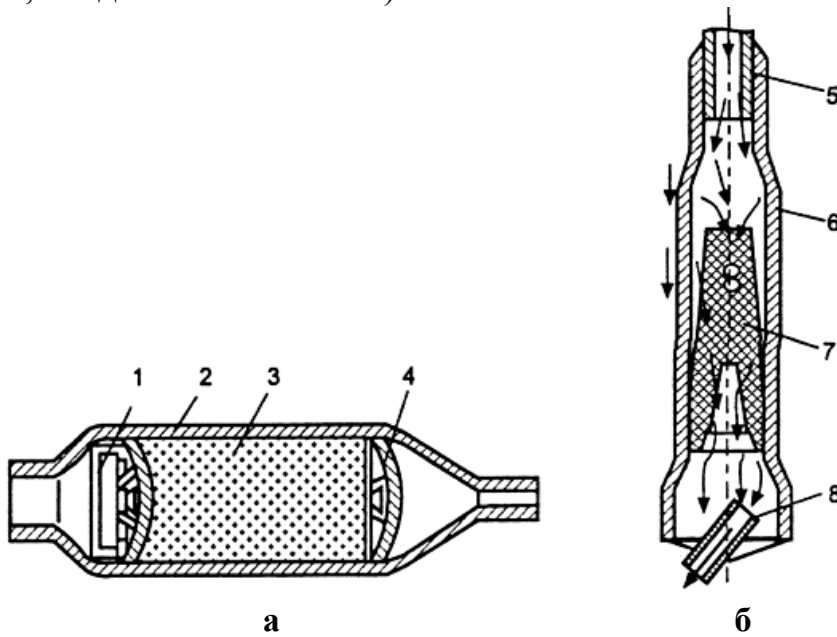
Фільтр-осушувальний патрон: а – без металокераміки; б – з металокерамікою: 1 – обойма сітки фільтра; 2 – корпус; 3 – адсорбент; 4 – сітка фільтра; 5 – трубка конденсатора; 6 – корпус; 7 – фільтр; 8 – капілярна трубка
